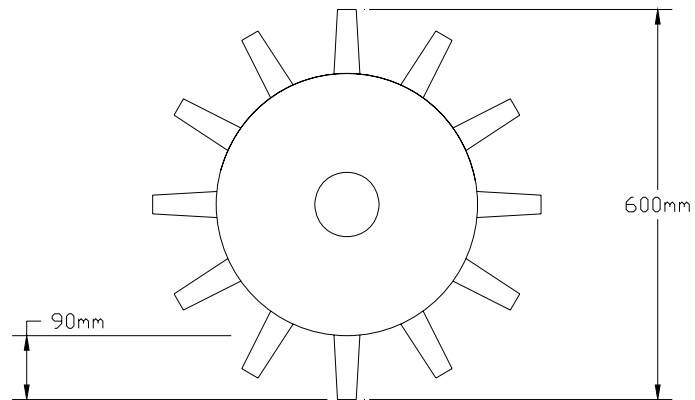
Layout da roda puncionadora e suas principais dimensões.
